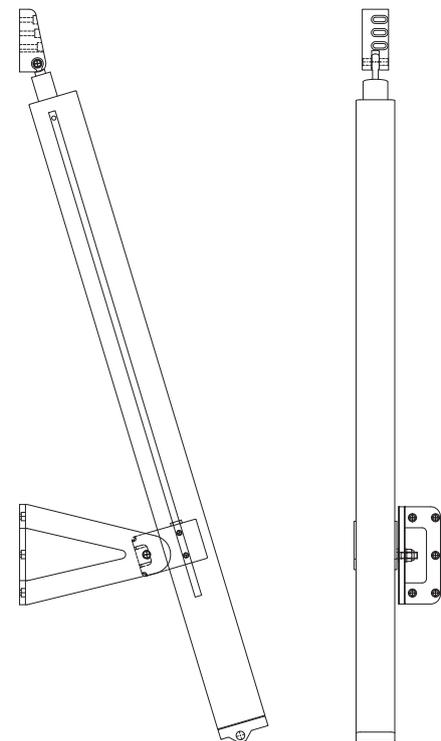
Spindeltrieb Typ G mit montierter oberer und unterer Montagekonsole mit versetzter (mittlerer) Aufhängung
